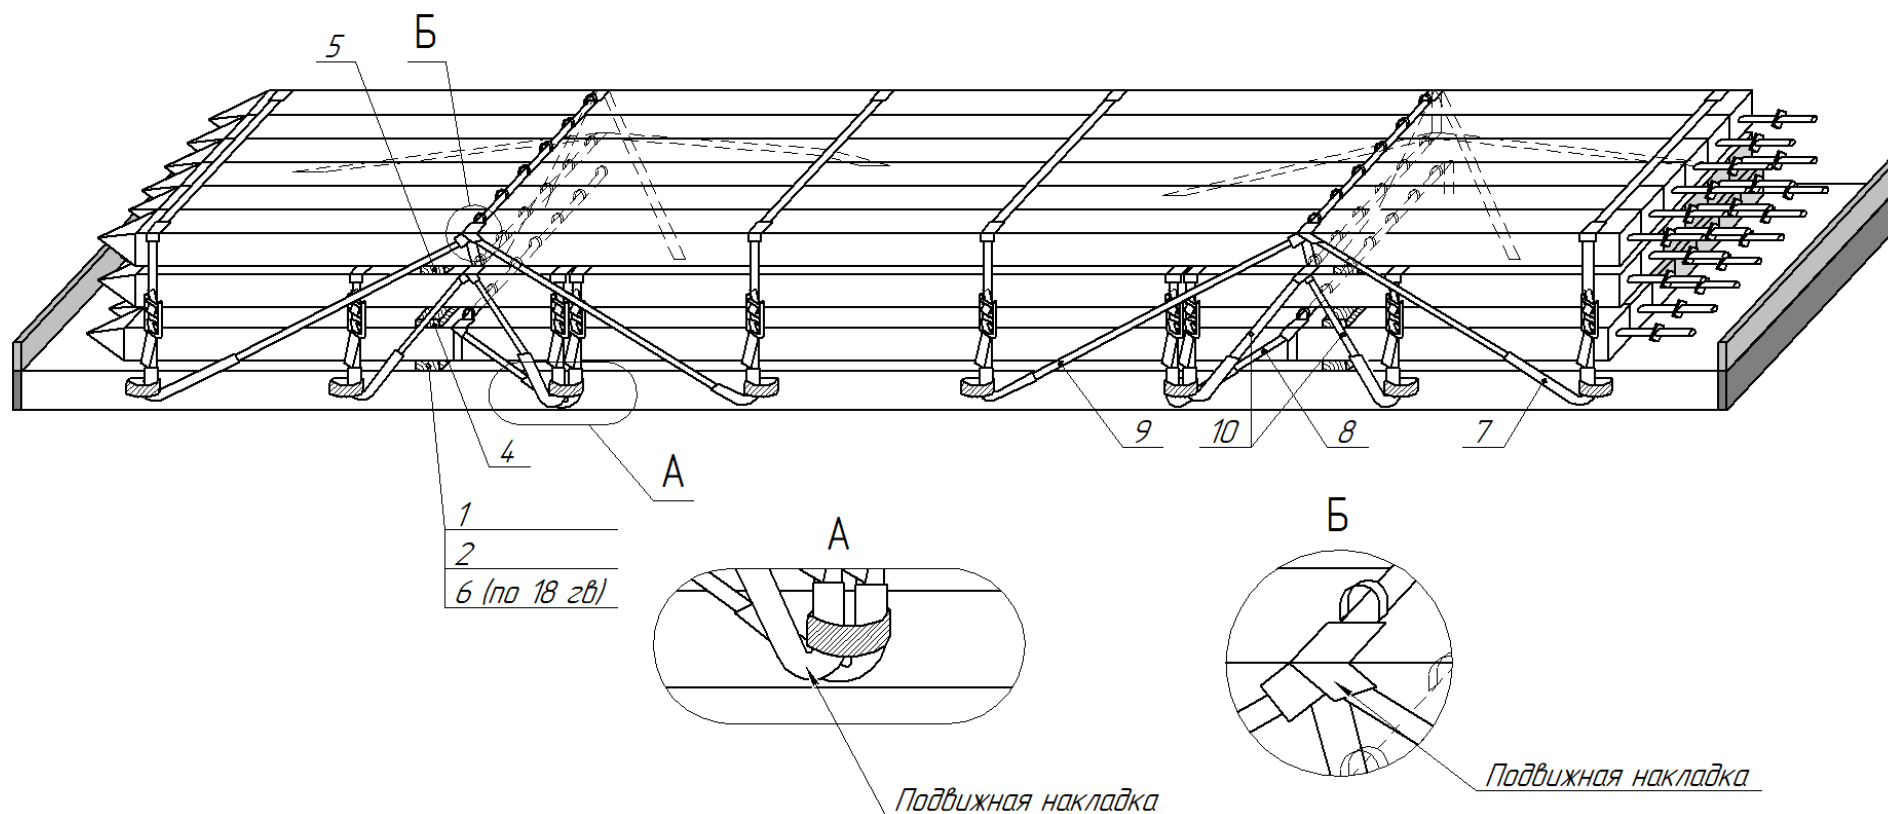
Изометрический вид примера размещения и крепления свай на платформе.
